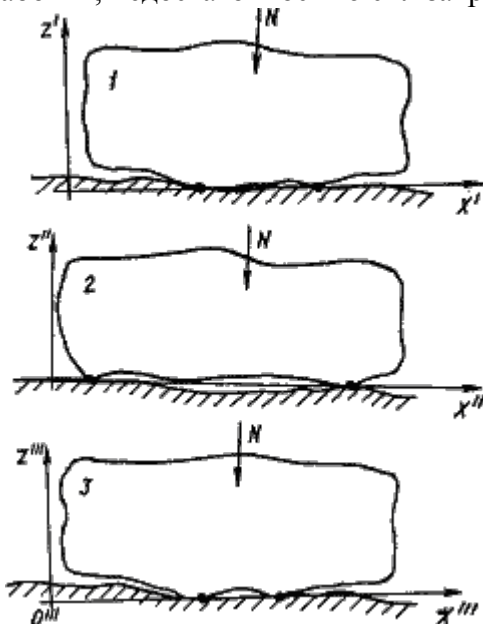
Случайное расположение точек контакта заготовки с базирующими элементами станка или приспособления
